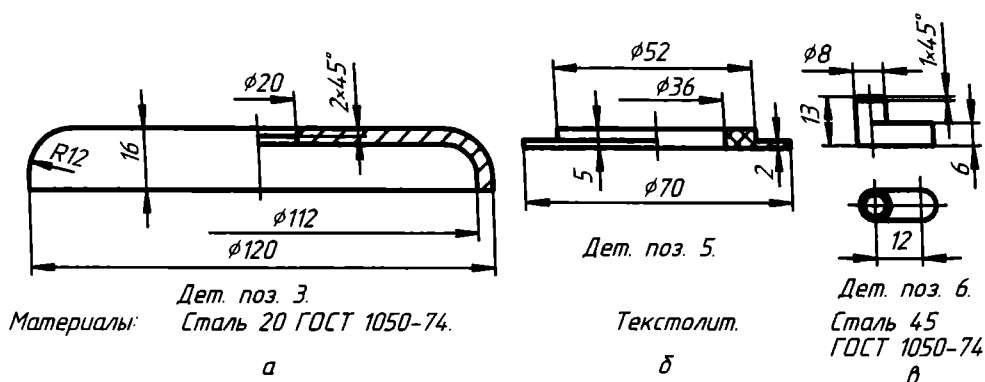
Чертежи: а — диска; б — шайбы; в — шпонки
